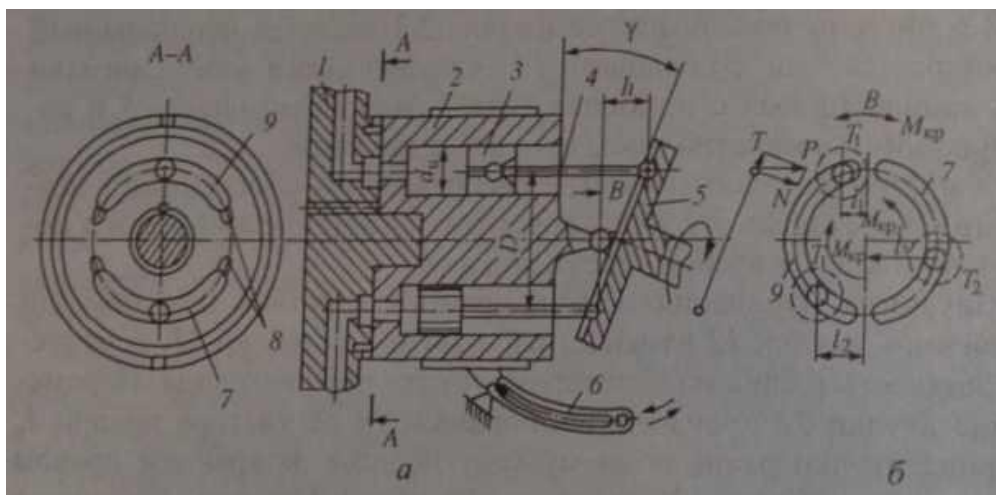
Схема аксиально-поршневого насоса-гидромотора с вращающимся цилиндрическим блоком с шарнирно связанными поршнями (сечение А-А условно повернуто на 90° по часовой стрелке):
